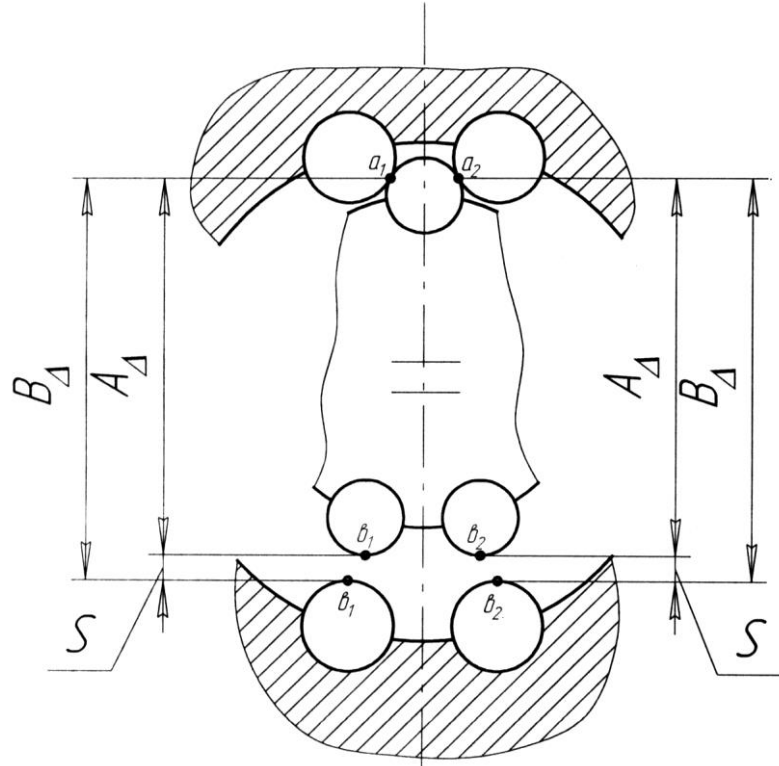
Сборочная размерная цепь силового соединения (вытеснителей) планетарного гидромотора
